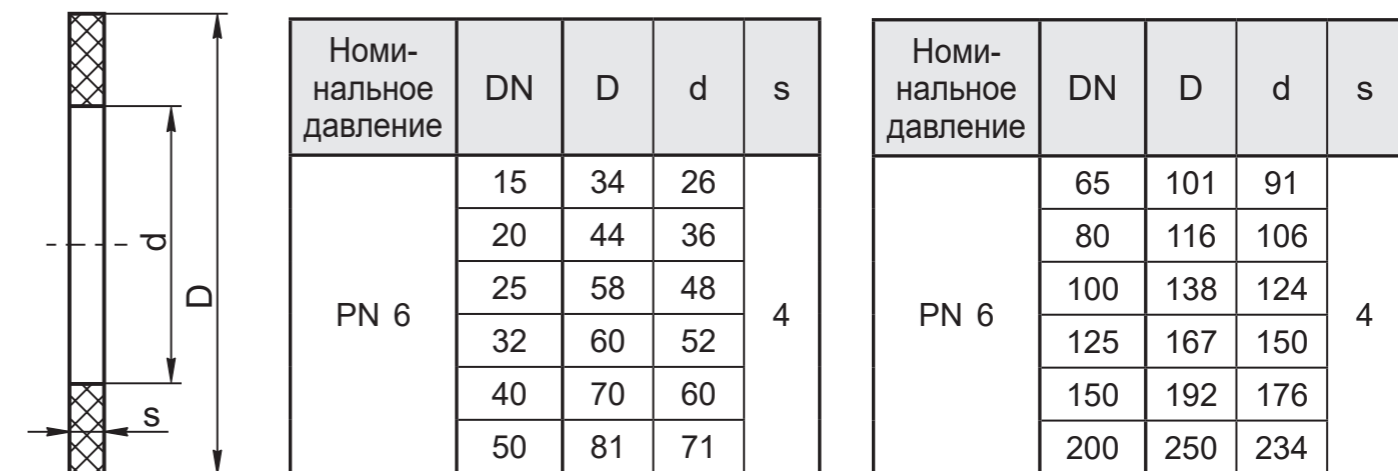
Прокладка из резины листовой марки МБС (для PN 6)
